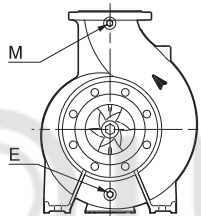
Пробка сливного отверстия и пробка отверстия для заливки насоса
